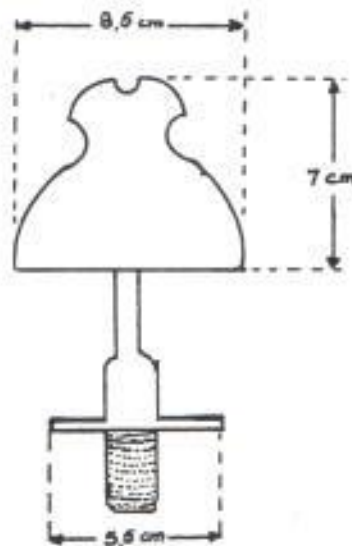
MEDIDAS DE UN AISLADOR TIPO ESPIGA
